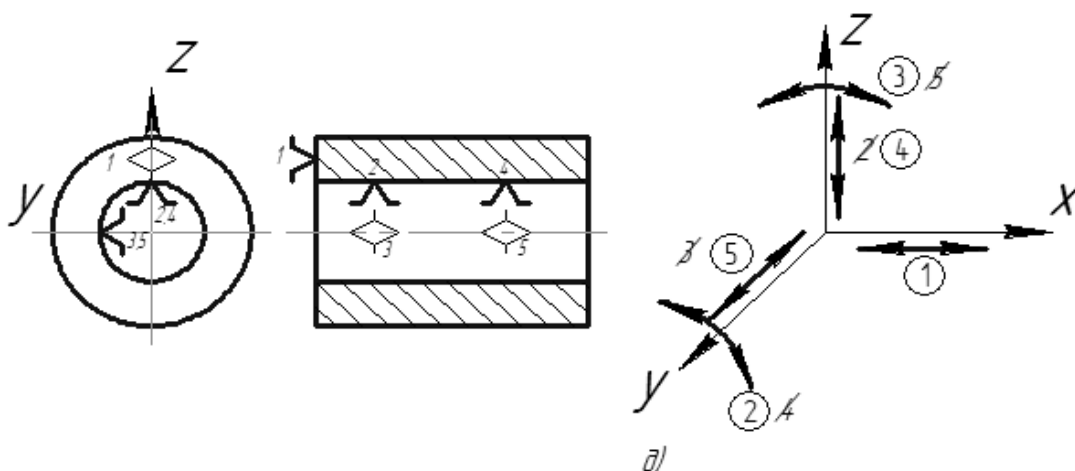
Базування циліндричної заготовки з центральним отвором на оправці
